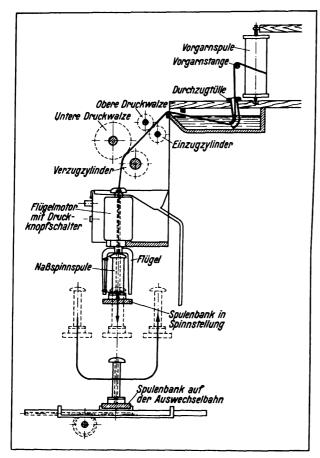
Schnitt durch eine Seite einer Schneiderspinnsmaschine (Naßspinnmaschine) mit motorischem Flügeltrieb und mechanischem Spulenwechsel.
